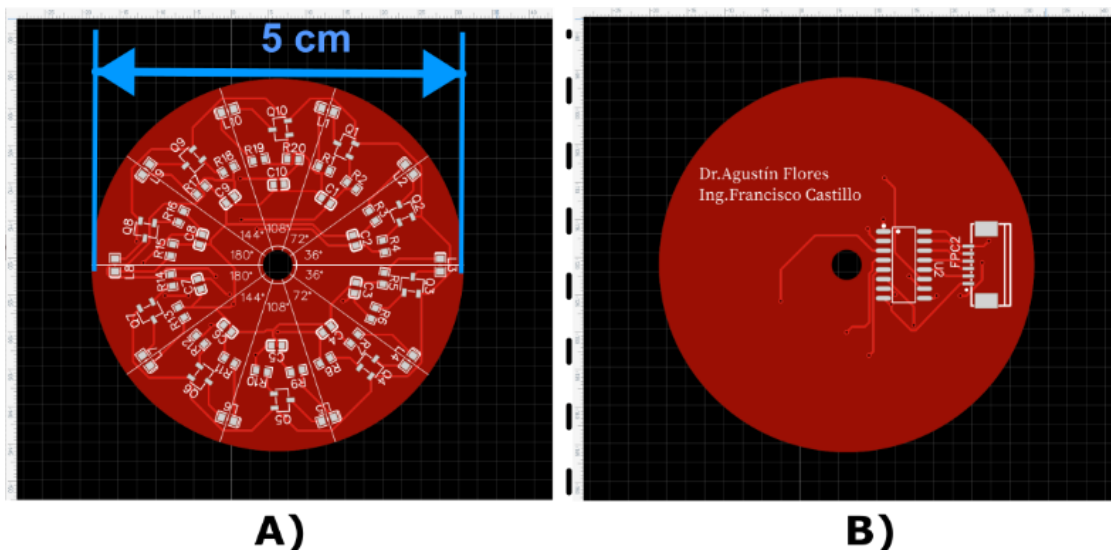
Vista en 2D de PCB diseñada. A) Vista de la primera capa y B) Vista de la segunda capa. Elaboración propia (2025).
